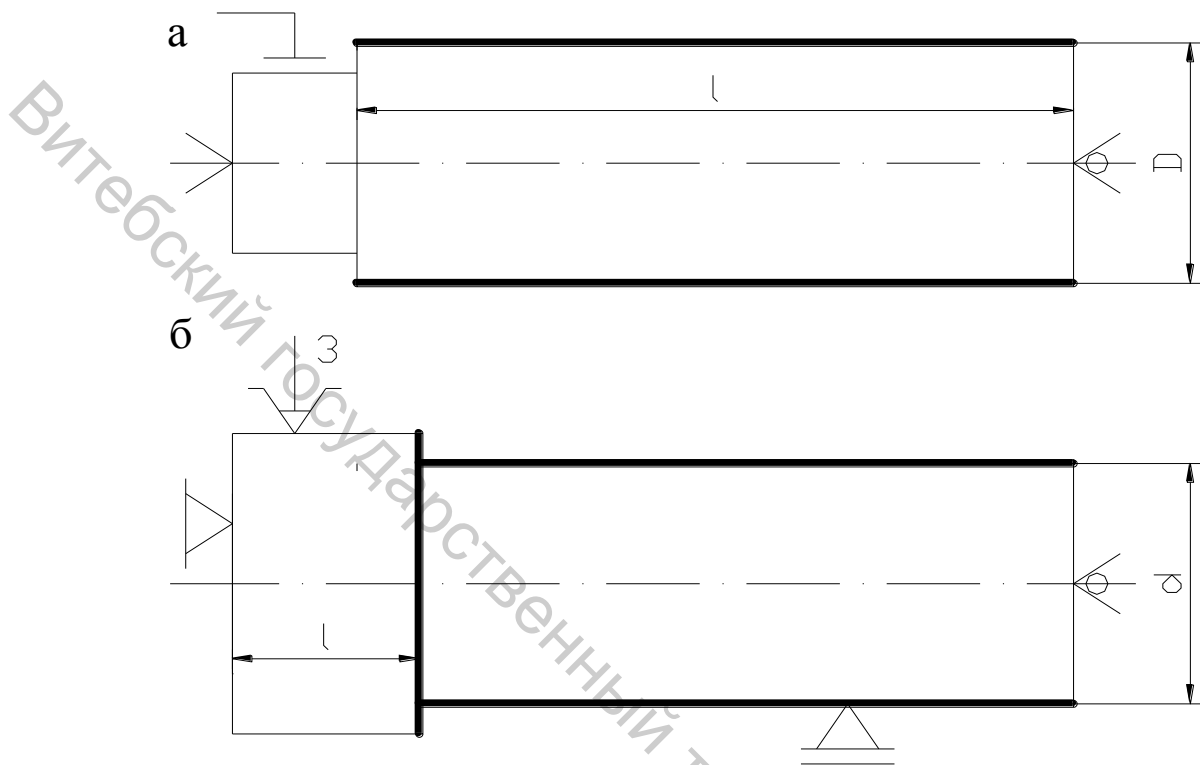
Схемы установки цилиндрических заготовок:
